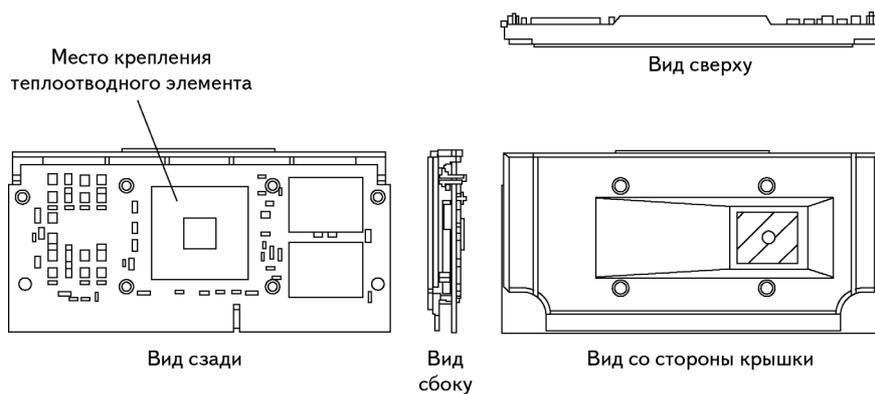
Корпус SECC2 процессоров Pentium II/III
